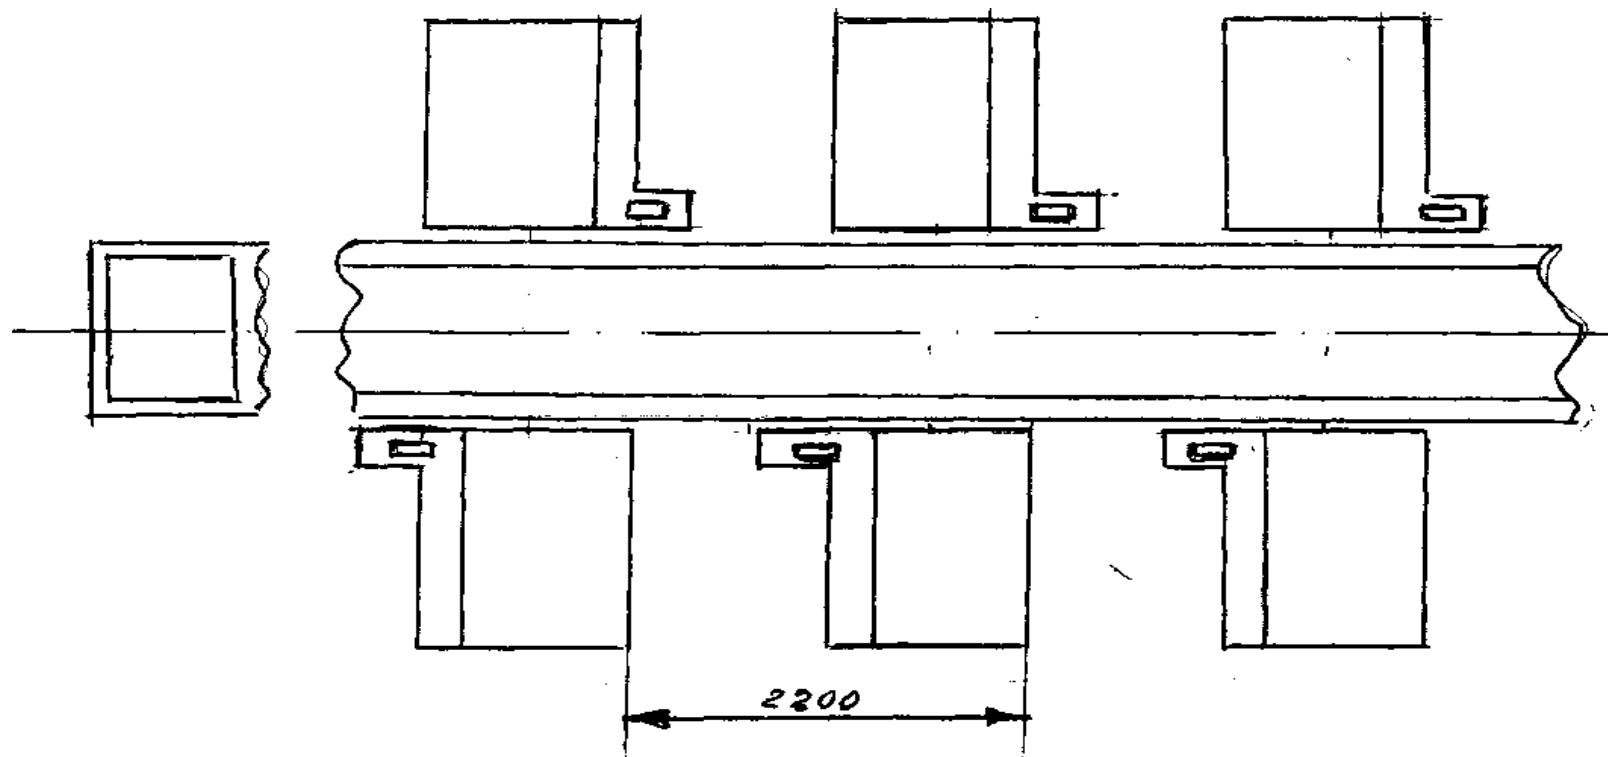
Схема установки прессов типа ПКП-10 относительно конвейера КЗЛ-О, вид сверху
